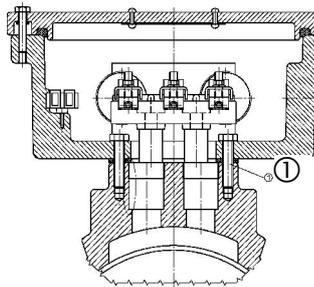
Klemmenkasten mit Befestigungsschraube ①
